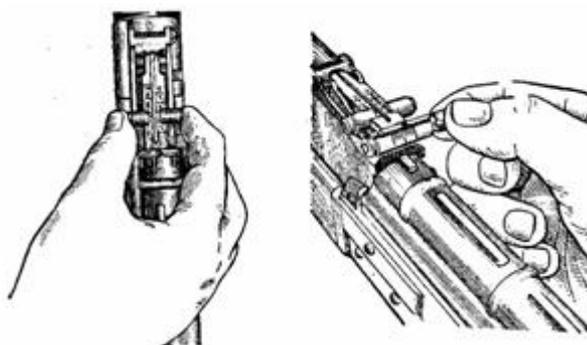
Установка прицела; Рисунок 23.7. Установка целика
